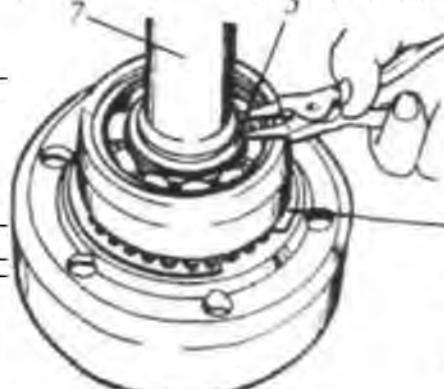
Знімання стопорного кільця 5 з вала 7 коронної шестерні 1.
